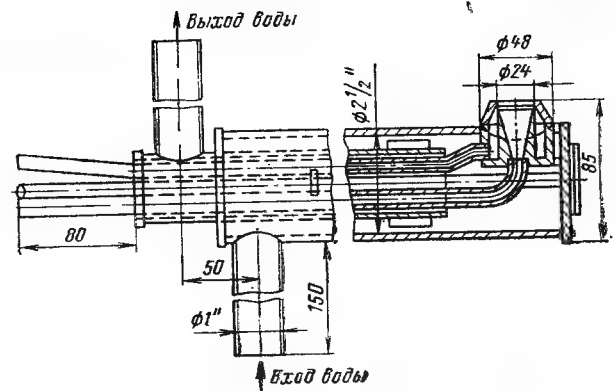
Трубка для отбора проб пыли и газа из топки.
